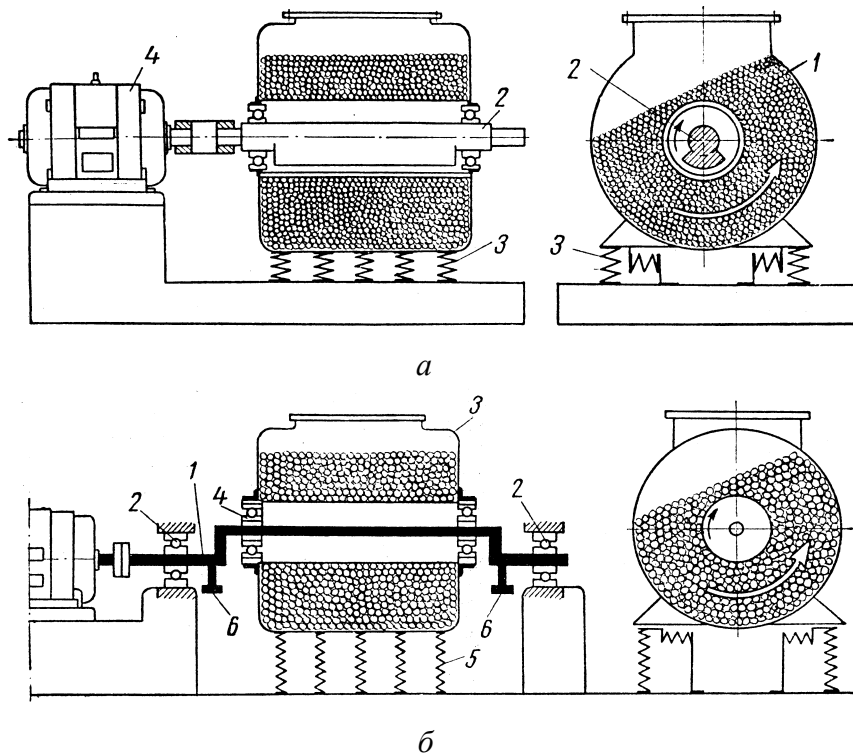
Схема вібраційних млинів: а – інерційного (1 – корпус; 2 – дисбалансний вал; 3 – пружина; 4 – привід); б – гіраційного (1 – ексцентриковий вал; 2, 4 – підшипники; 3 – корпус; 5 – пружина; 6 – противага)
